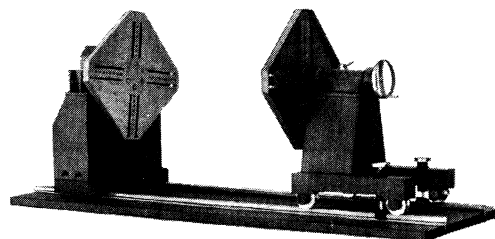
Сварочный горизонтальный вращатель МЗ1070А
